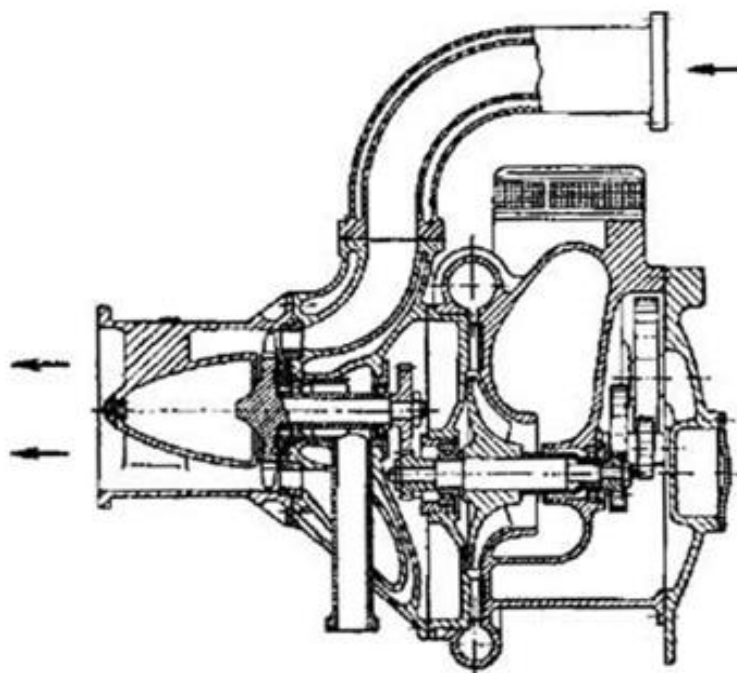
Турбокомпрессора Т9-29 двигателя Дельтик
